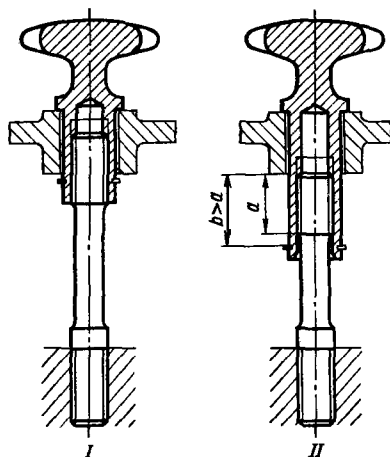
«Нетеряющиеся» гайки. Случай крепления крышки к корпусу
